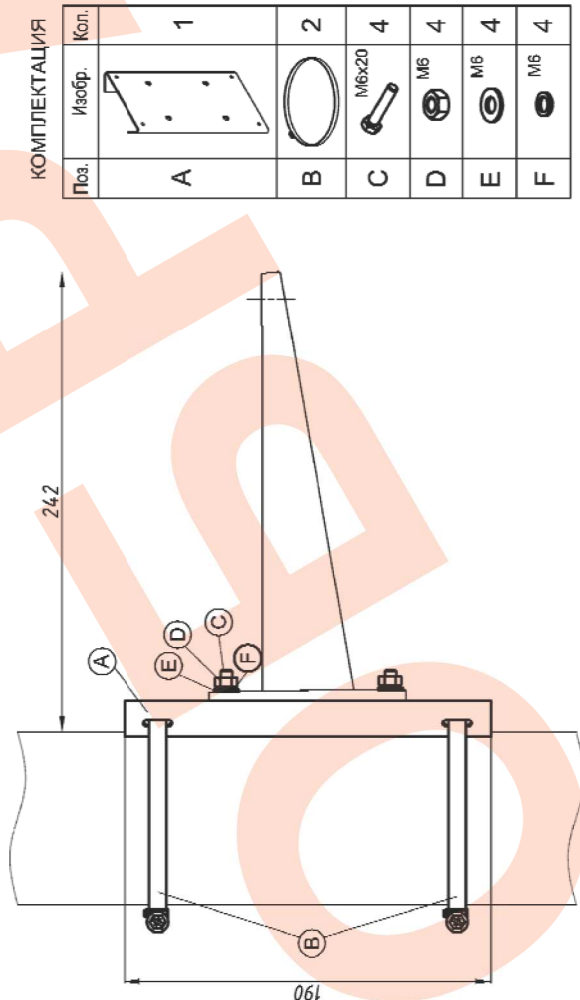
Монтаж кронштейна КС-1 на опору (круглую или квадратную)
